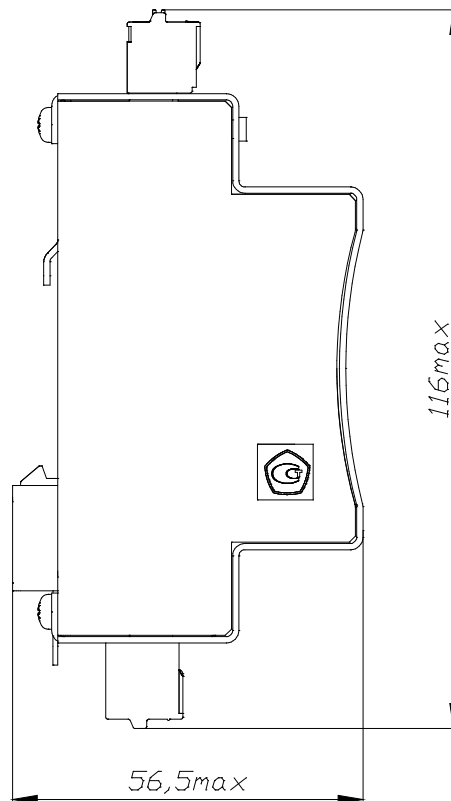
Модуль УВВ. Габаритный чертеж. Вид сбоку
